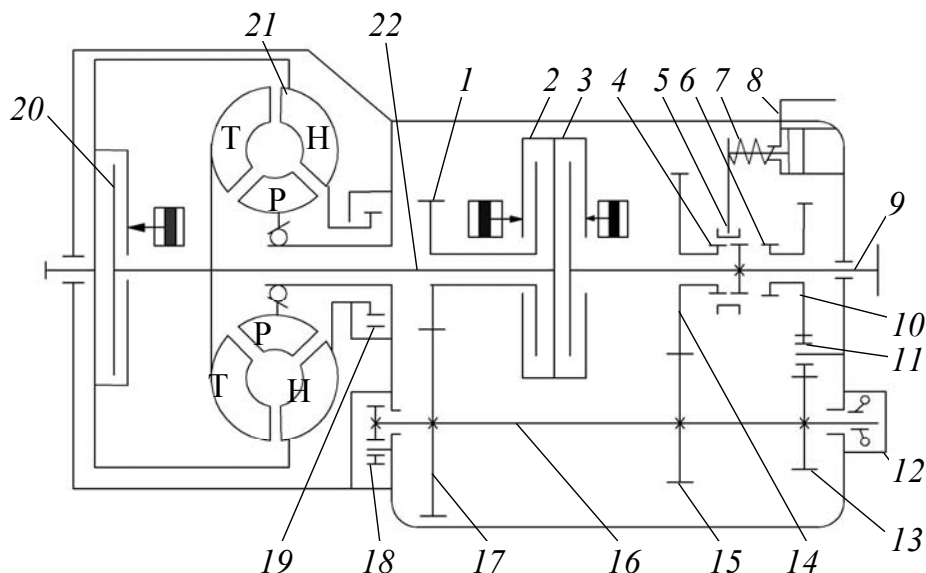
Схема гидромеханической передачи с двухступенчатой коробкой передач (двухскоростной):
